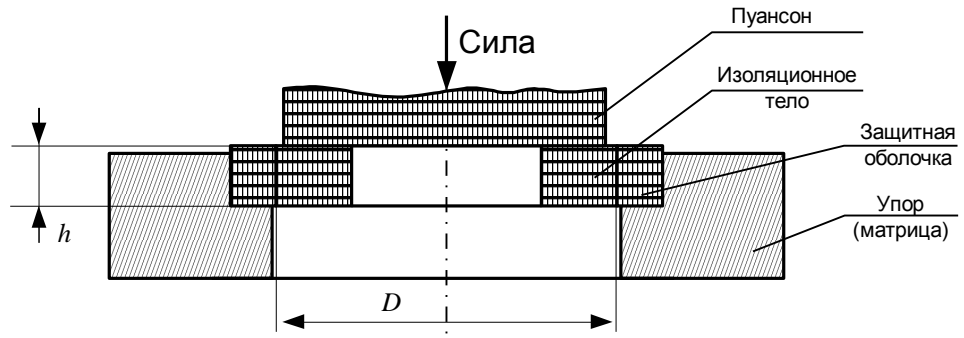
Образец изолятора и приспособления для испытаний методом сдвига
